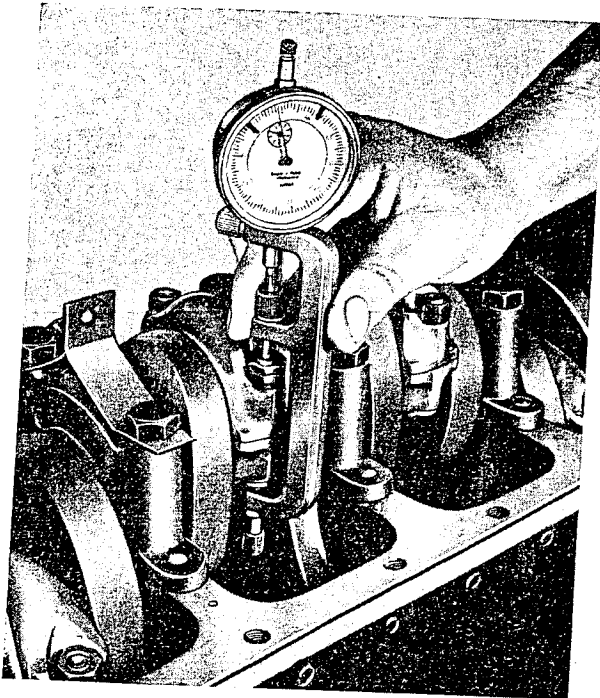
Nach einem Anzug von 3,75-3,80 mkg wird die Dehnung der Pleuelschraube gemessen. Die Dehnung soll 0,1 mm betragen (die Messung ist ohne Sicherungsblech vorzunehmen)
